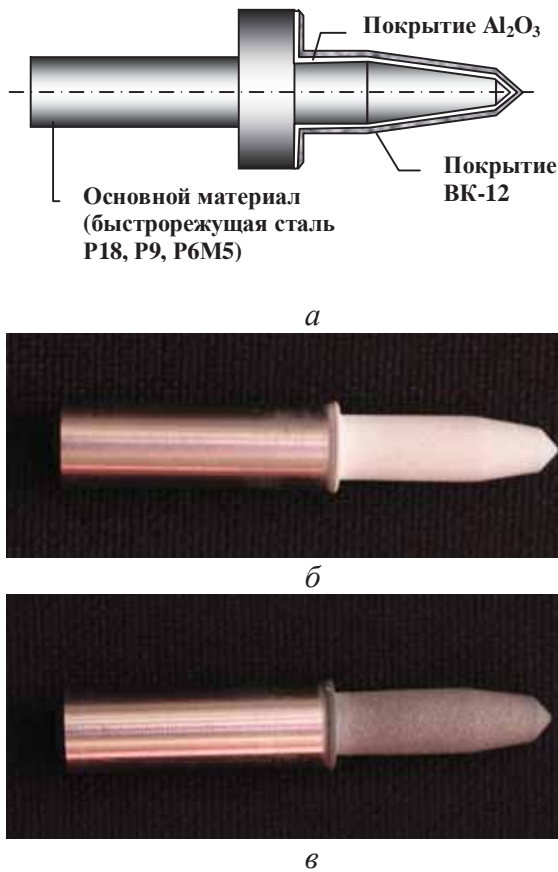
Пуансон для пластического сверления: а – схема расположения слоев покрытий; б – напыление на стальную заготовку теплоизолирующего керамического подслоя; в – нанесение на керамику внешнего износостойкого твердосплавного покрытия
